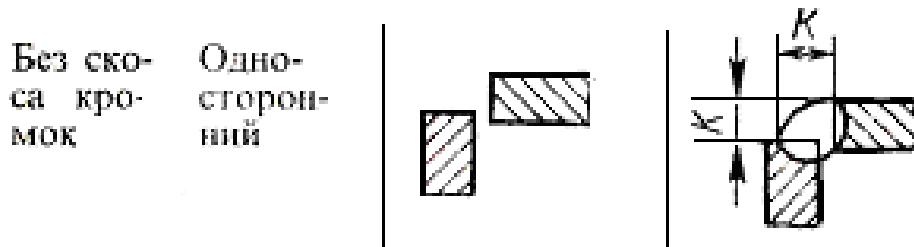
Виды сварных угловых соединений
